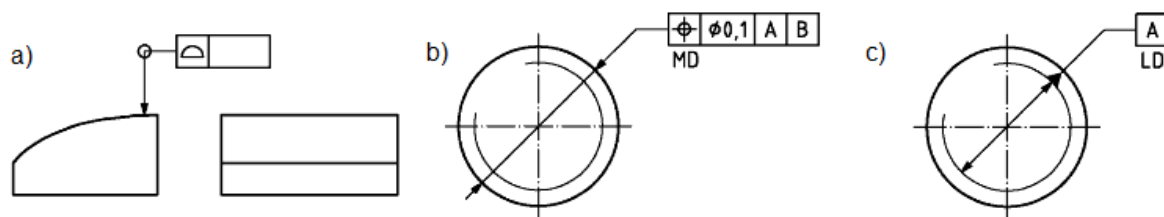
Specyfikowanie bazy lub tolerancji dla ograniczonego obszaru elementu
